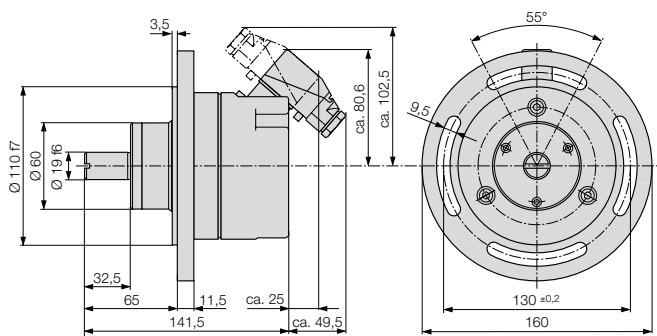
KINAX WT 707 mit Steckverbinder und Flansch.
